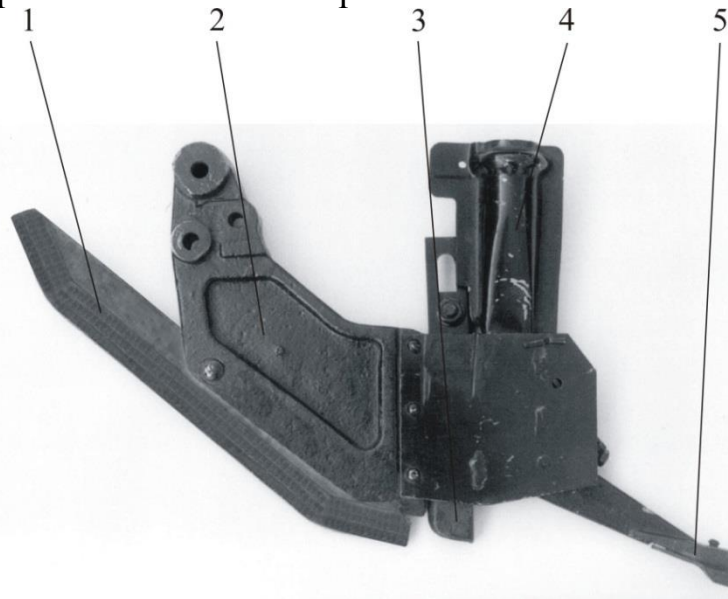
Полозковий сошник зернової сівалки зі зміцненим полозом: 1–полоз; 2–корпус; 3–ущільнююча п'ятка; 4–раструб; 5–загортаюча п'ятка
